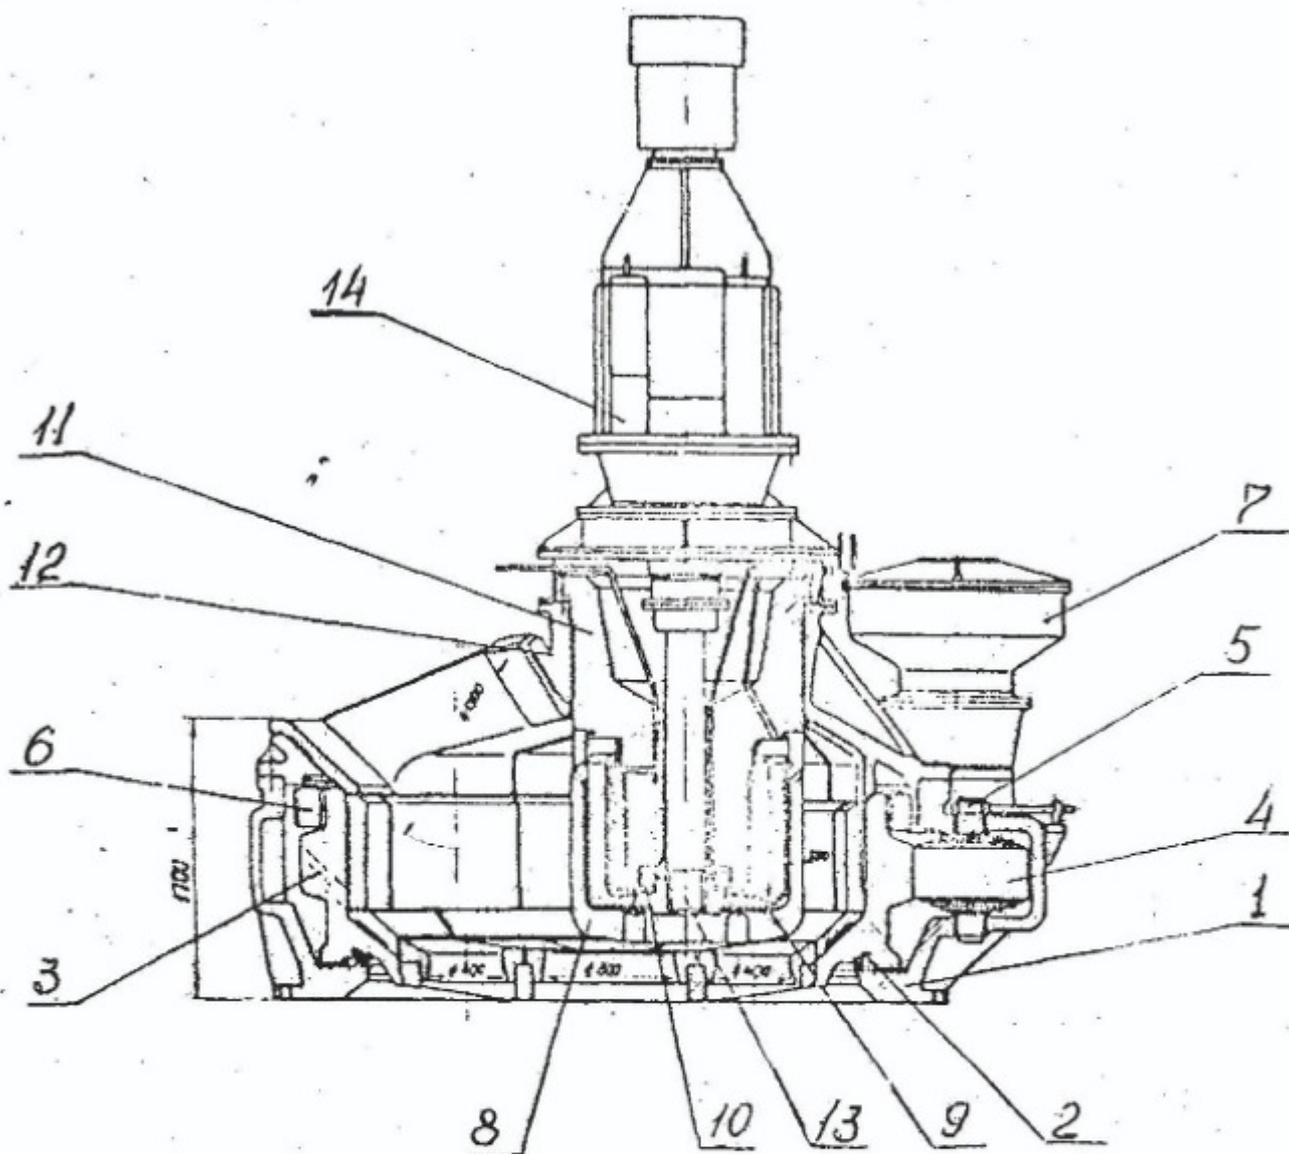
Конструктивная схема дробилки крупного дробления внутривалкового типа с цилиндрическими телами дробления
